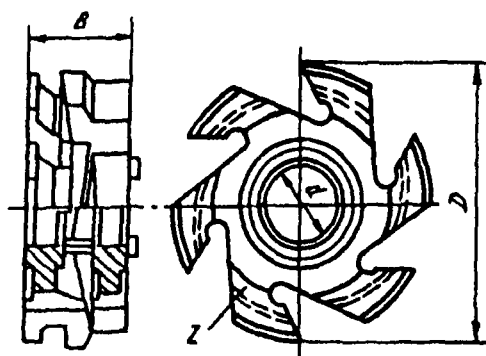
Пример фрезы для обработки окон (фасонная с затылованными зубьями для обработки брусков створок и коробок)
